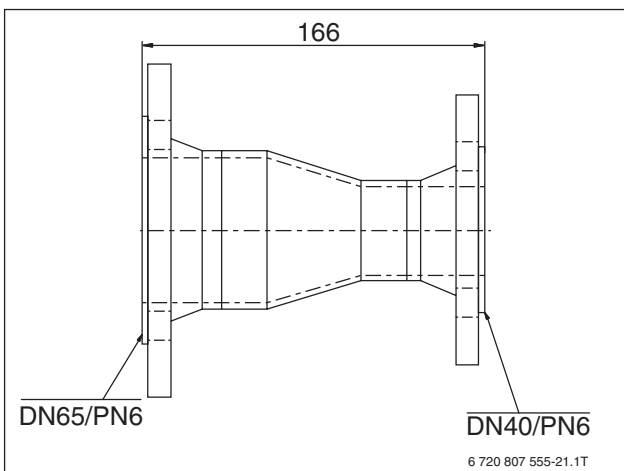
Anschlussstück DN 65/PN 6 – DN 40/PN 6
